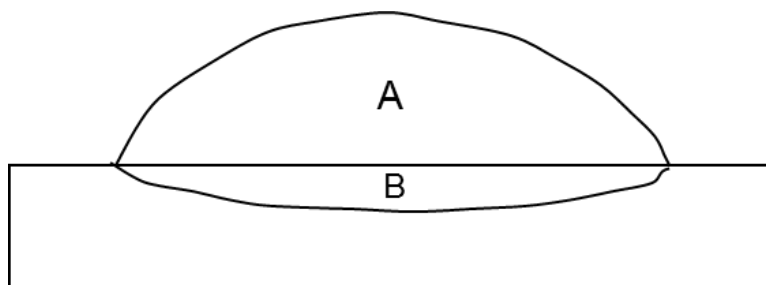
Perfil de soldadura para cálculo de dilución.
